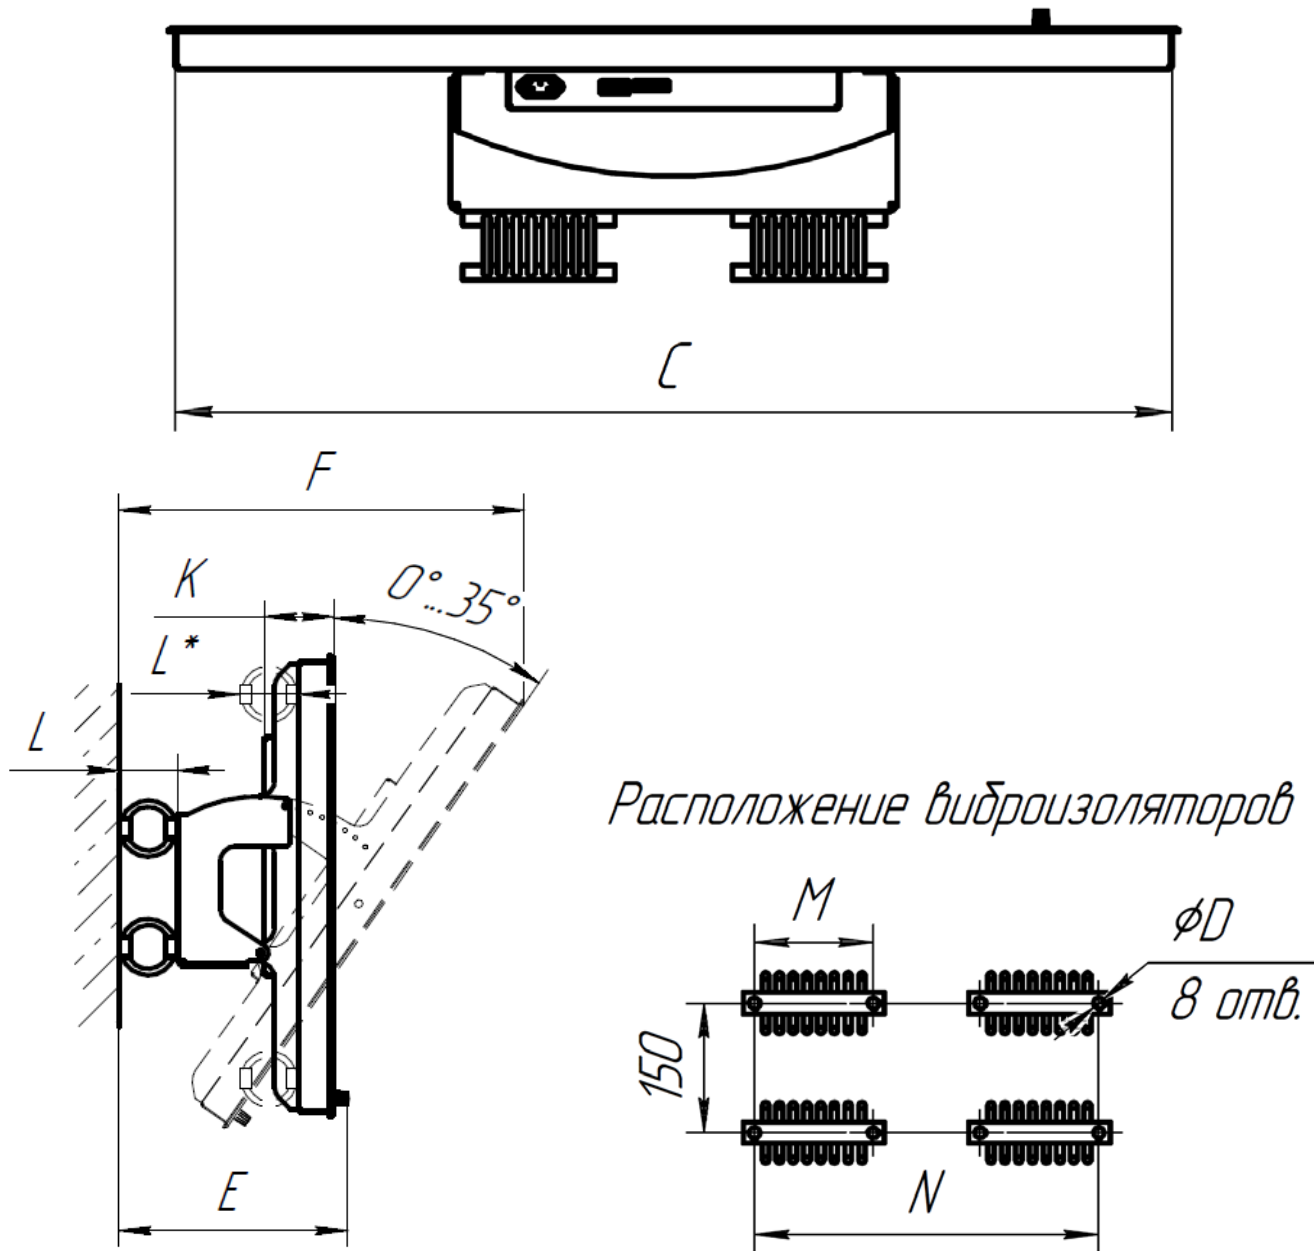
Габаритный чертеж устройства с виброизоляторами
